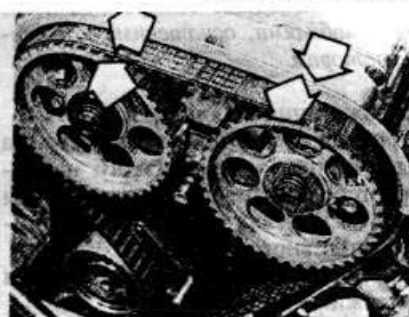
Метки на звездочке распредвала совпадают с рисками на крышке — двигатель с двумя распредвалами
